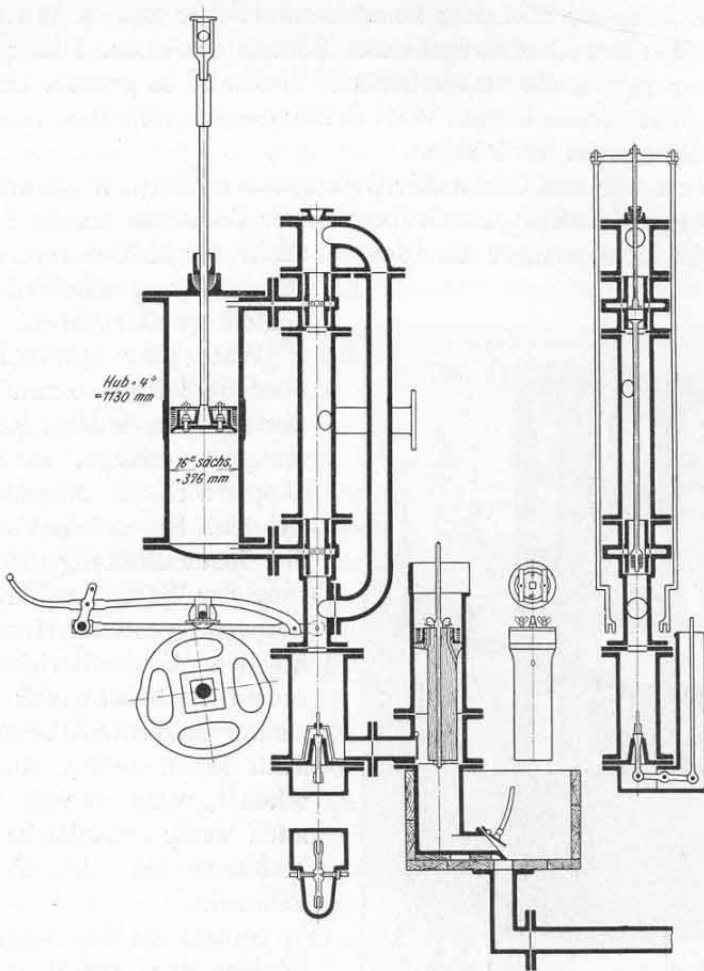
und 319. Steuerung zur Maschine Fig. 316.
